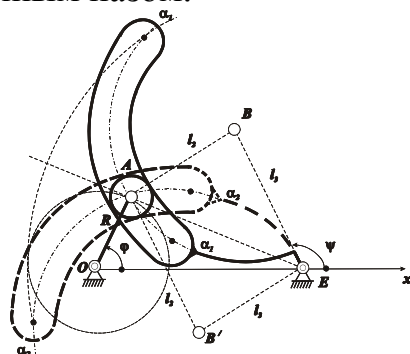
Кулисный механизм с криволинейным пазом с качательным движением выходного звена
